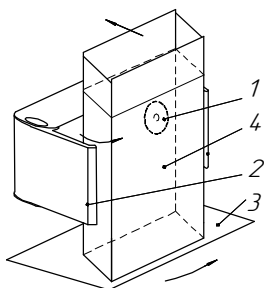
Формоутворення заготовки картонної пачки в карманному носії протягуванням по захвату: 1 - вакуумний захват, 2 - поворотні захвати, 3 - нижнє несуче дно, 4 - заготовка картонної пачки
